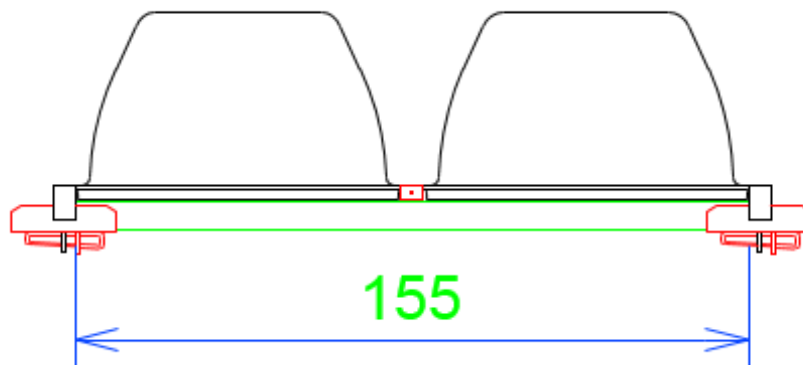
Seção adotada para o cálculo, demonstrando o vão útil da travessa
